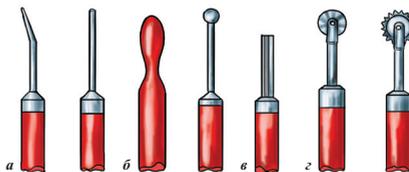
Инструменты для тиснения на фольге: а – линейник; б – выдавка шарообразная; в – пуансон (верхняя часть металлопрокатного штампа); г – накатка
